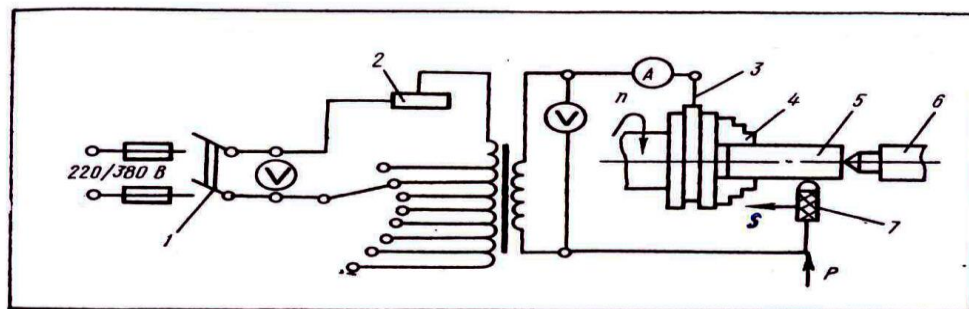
Схема электромеханической установки: 1-рубильник; 2-реостат; 3-скользящий контакт; 4-патрон; 5-обрабатываемая деталь; 6-задняя бабка; 7-инструмент
